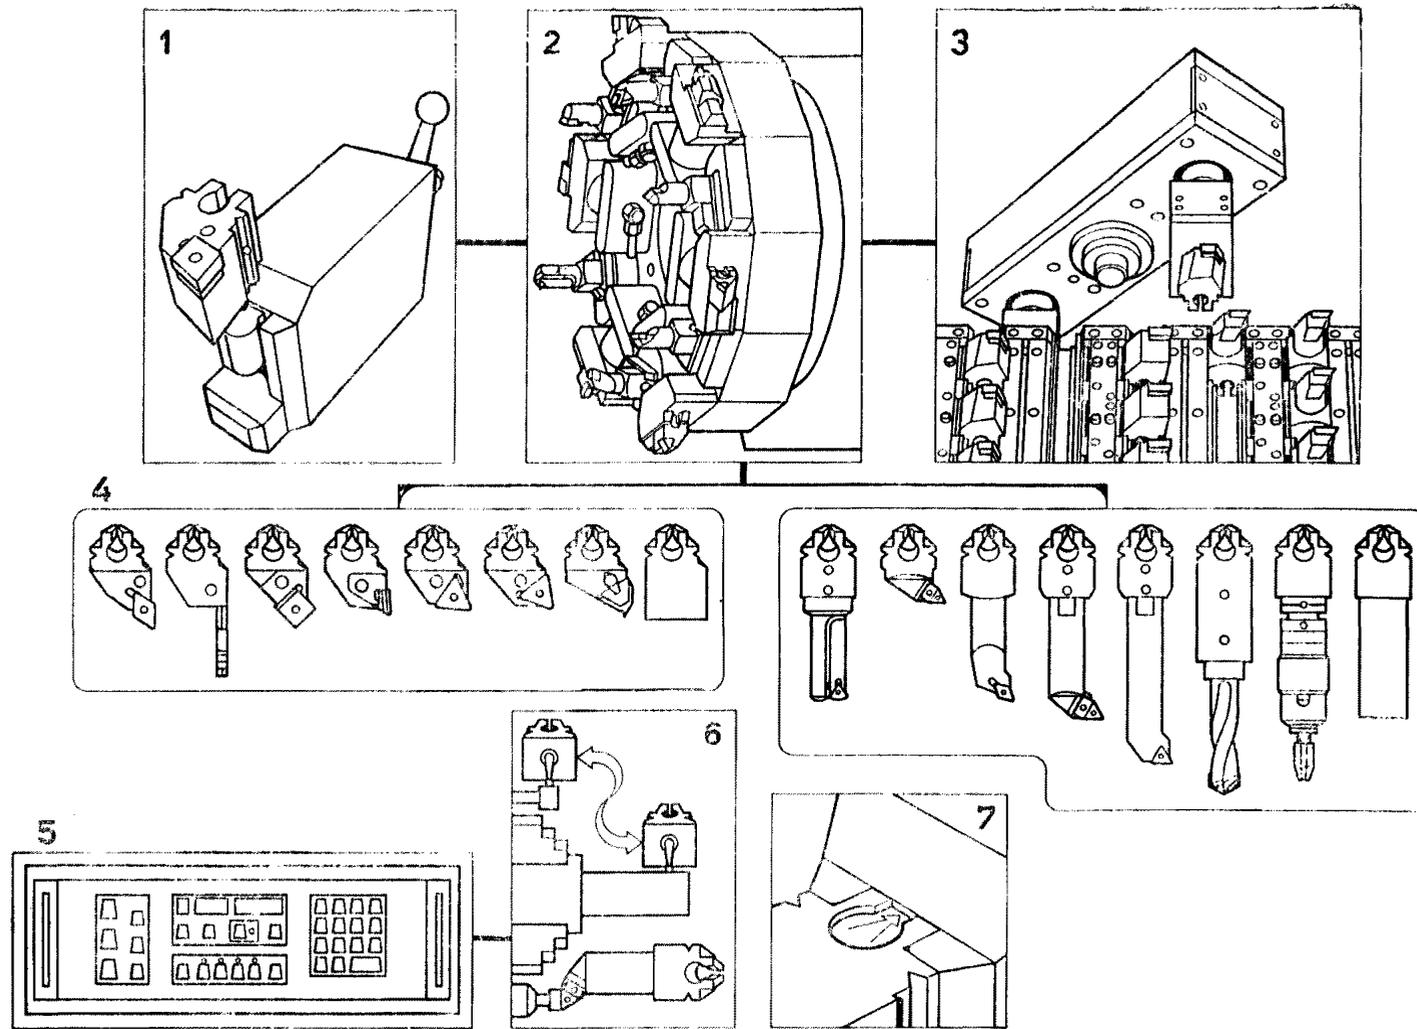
Пример установления стандартных присоединительных поверхностей, обеспечивающих единство блочно-модульного метода агрегатирования в ЦКИ для станков токарной группы:
